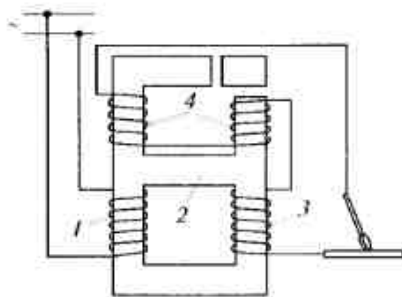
Электромагнитная схема сварочного трансформатора со встроенным реактором:
